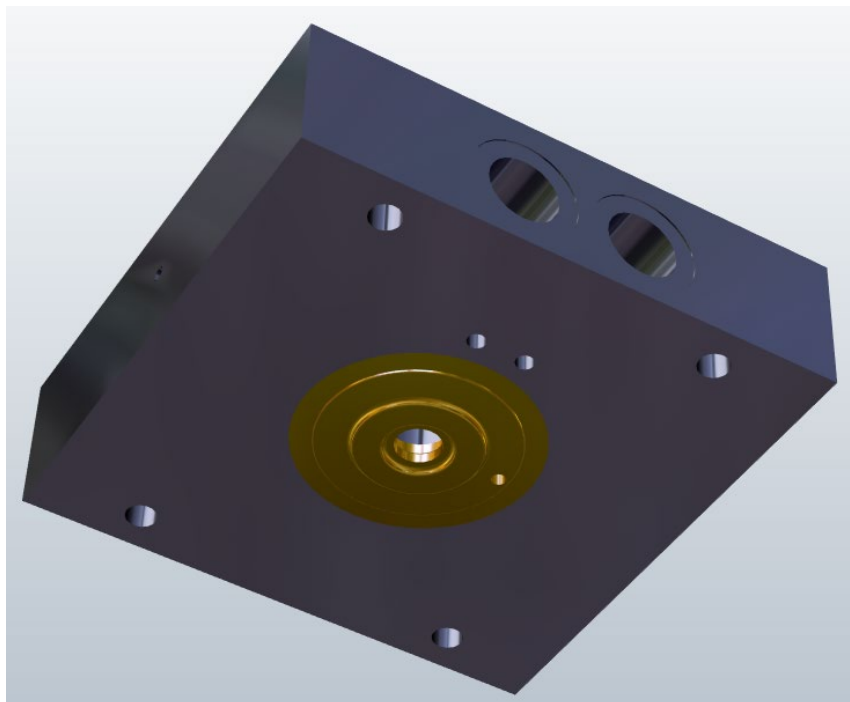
Partes de molde de inyección de plástico [B-44]
